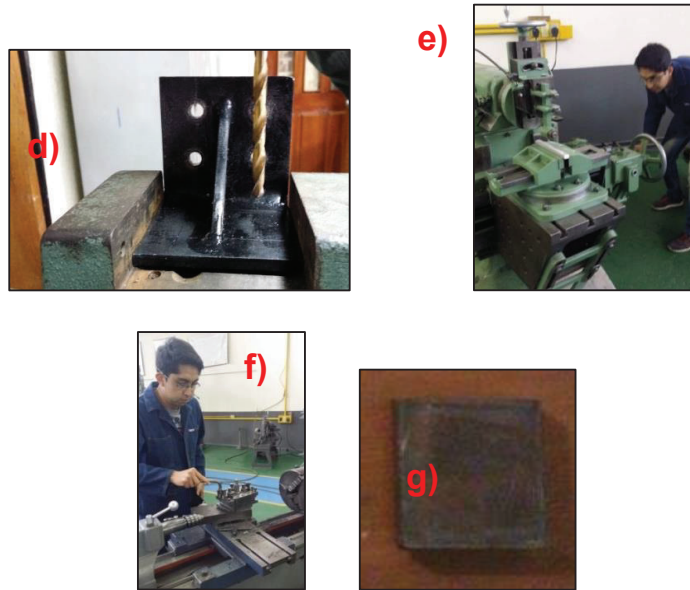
d) Taladrado de bisagras, e) Laminado de apoyos, f) Torneado de ejes para apoyos y eje de transmisión, g) Placa de dimensiones 60x20x60mm.
